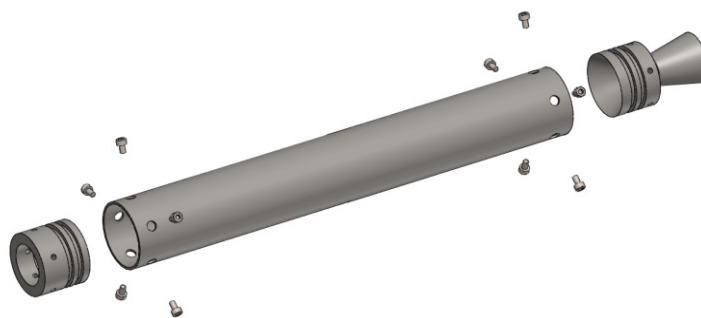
Vista explodida da montagem do motor-foguete feito no software SolidWorks.
